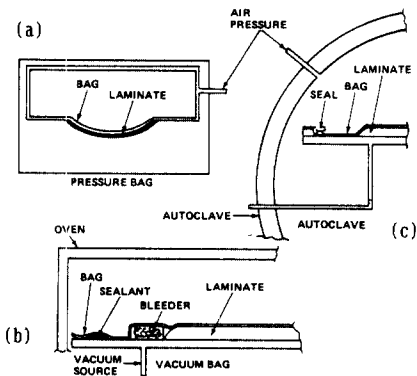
Bag molding 공정 (a) Pressure bag molding (b) Vacuum bag molding (c) Autoclave molding
